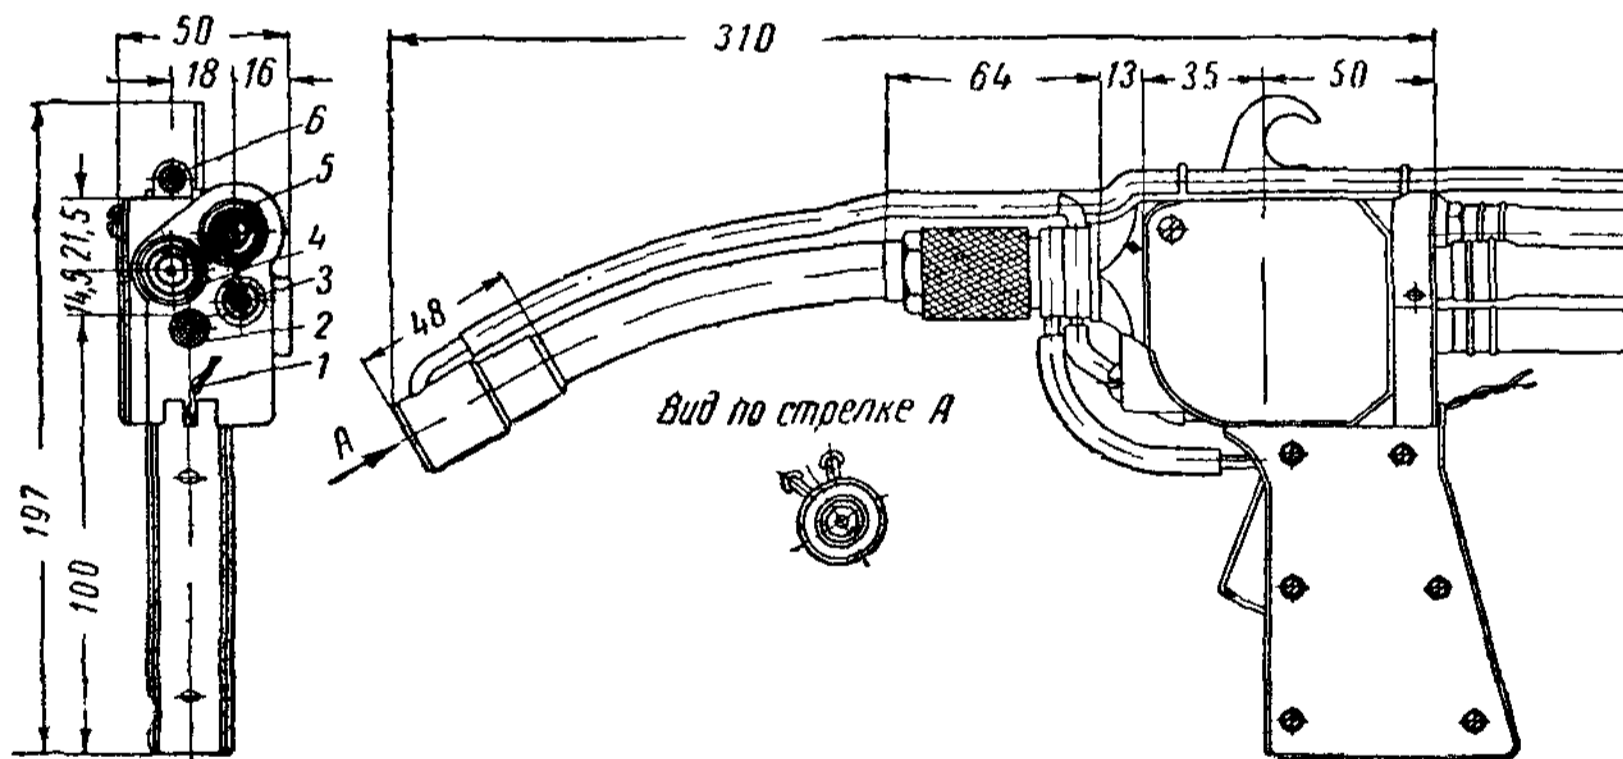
Сварочная горелка (пистолет) полуавтомата ПШПА-7 (НИАТ)
